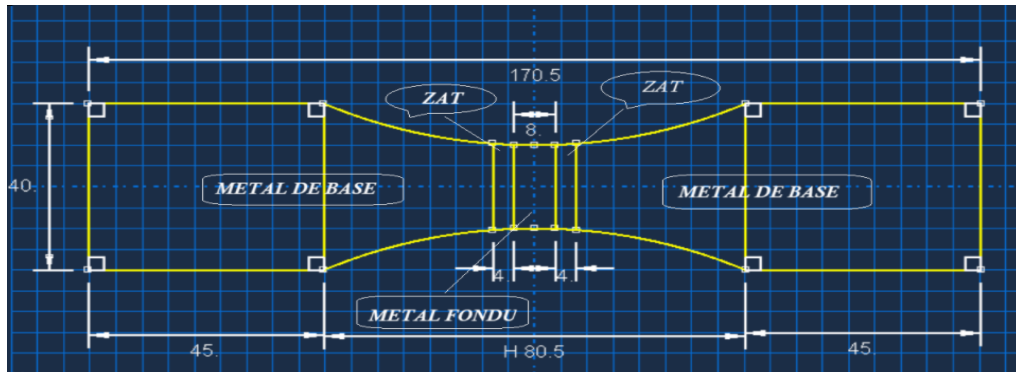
Dimensions de l'éprouvette soudée.
